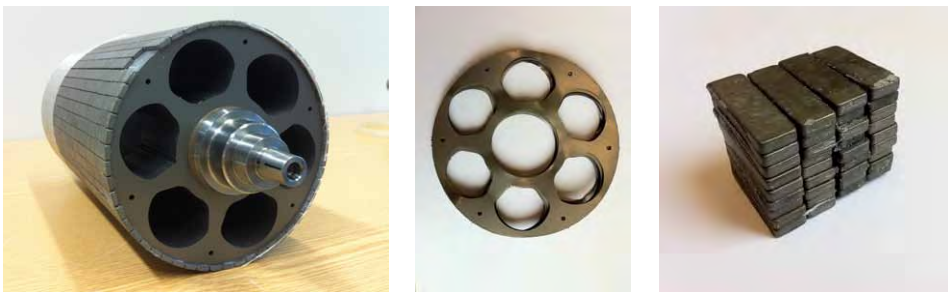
Rotor (links), Elektroleche (Mitte) und Magnete (rechts) eines Motors mit Oberflächenmagneten
